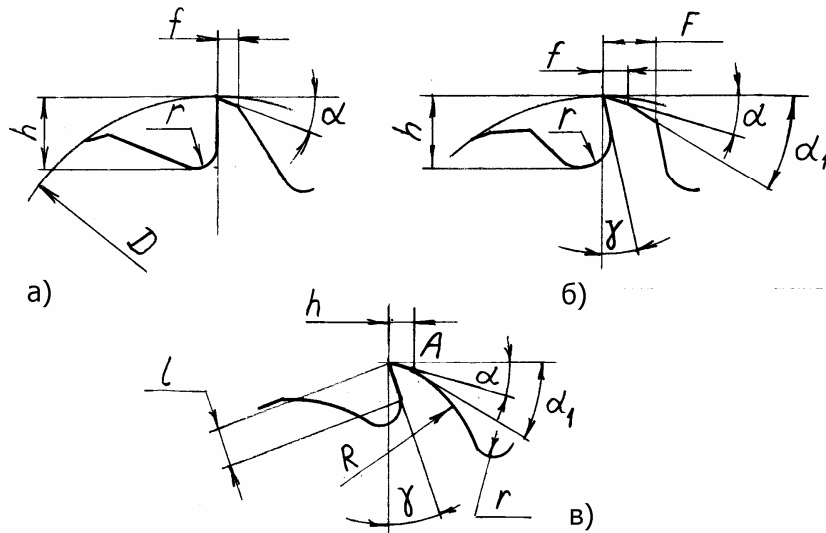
Форми зубців гострозаточених фрез:
